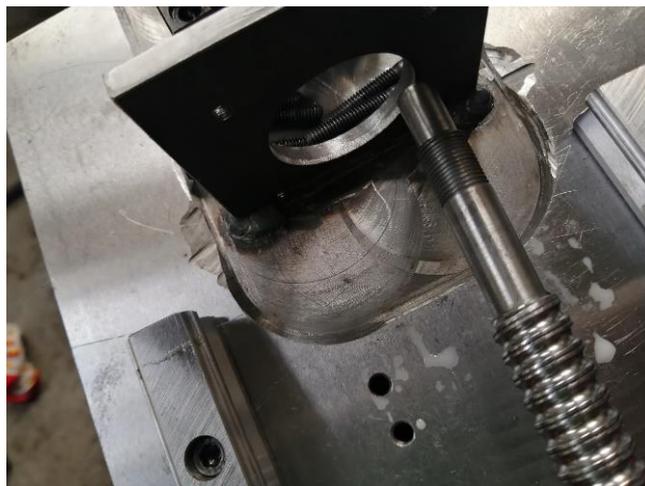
Soldadura de placa porta motor a bases
